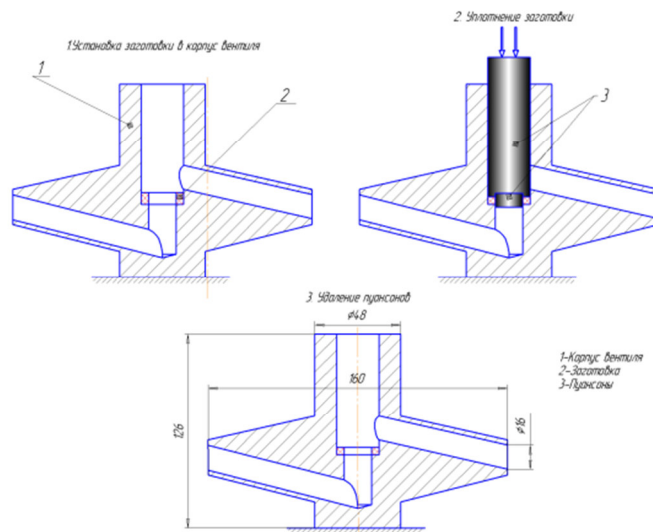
Схема процесса динамического горячего прессования в заготовке корпуса вентиля
